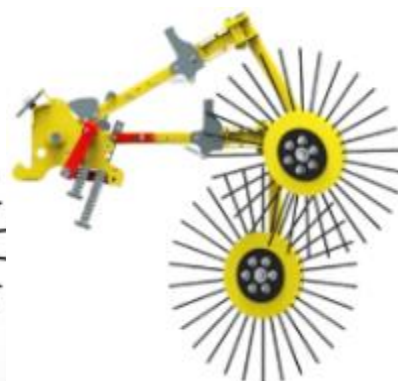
Sollevatore rapido attivato – Posizione sollevata
